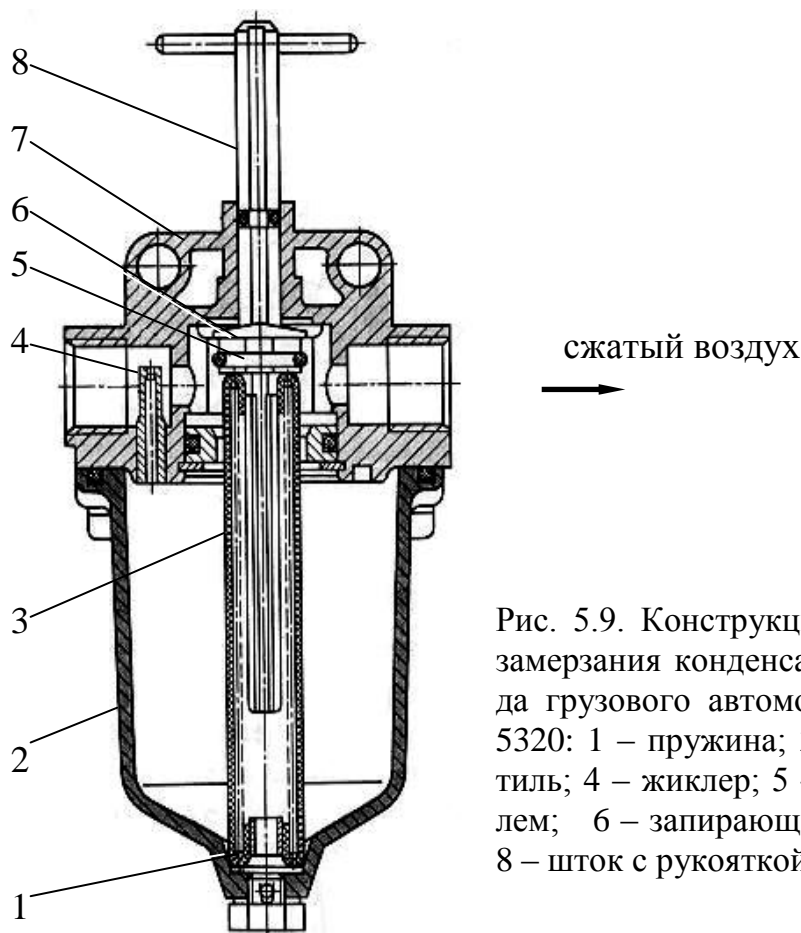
Конструкция предохранителя от замерзания конденсата тормозного привода грузового автомобиля-тягача КАМАЗ-5320: 1 – пружина; 2 – корпус; 3 – фитиль; 4 – жиклер; 5 – пробка с уплотнителем; 6 – запирающий штифт; 7 – корпус; 8 – шток с рукояткой
